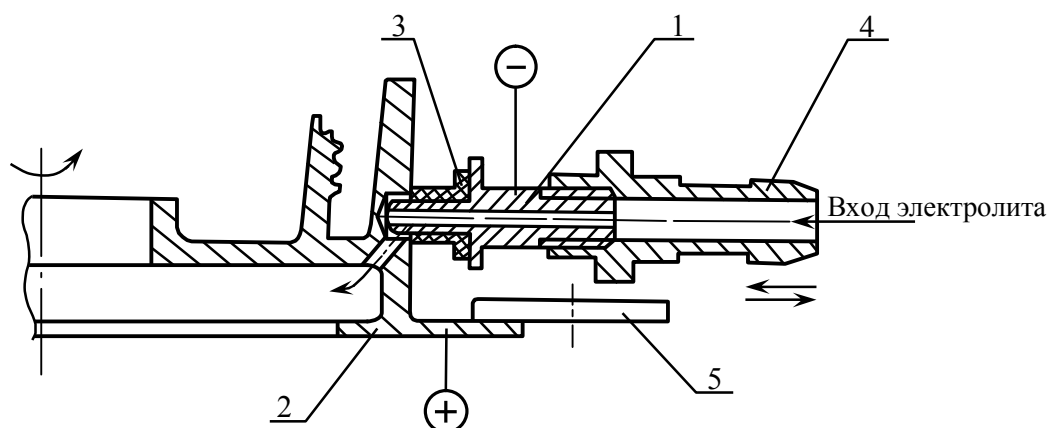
Схема скругления острых кромок в месте пересечения отверстий детали «Лабиринт двойной»: 1 – электрод – инструмент; 2 – деталь; 3 – изоляционная втулка; 4 – штуцер подвода электролита; 5 – прижим детали
